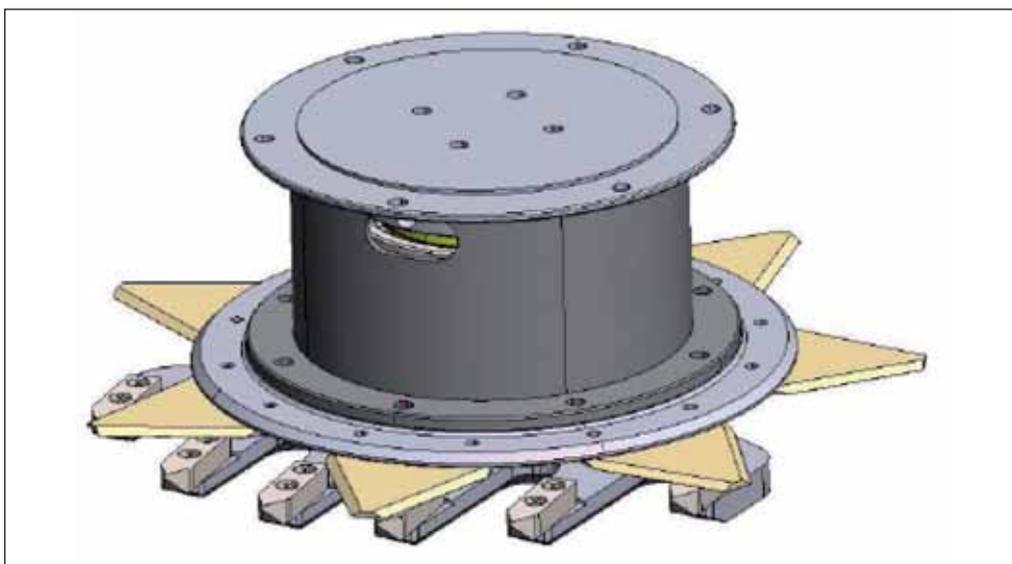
Particolare costruttivo dell'elemento sfalciante
